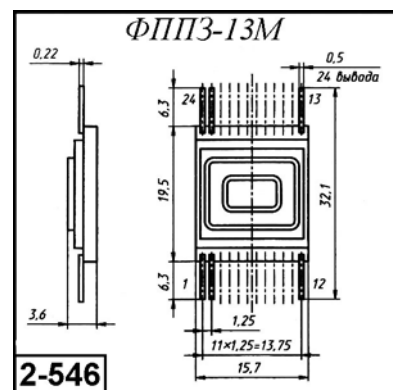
Внешний вид и габаритные размеры ФППЗ-13М
